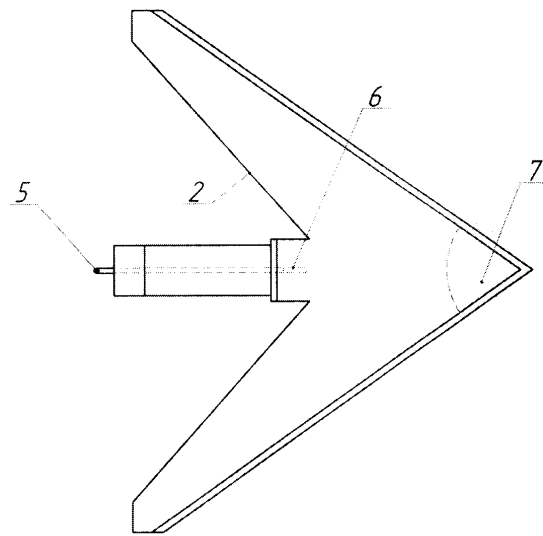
Общий вид культиватора-удобрителя (вид сбоку)
